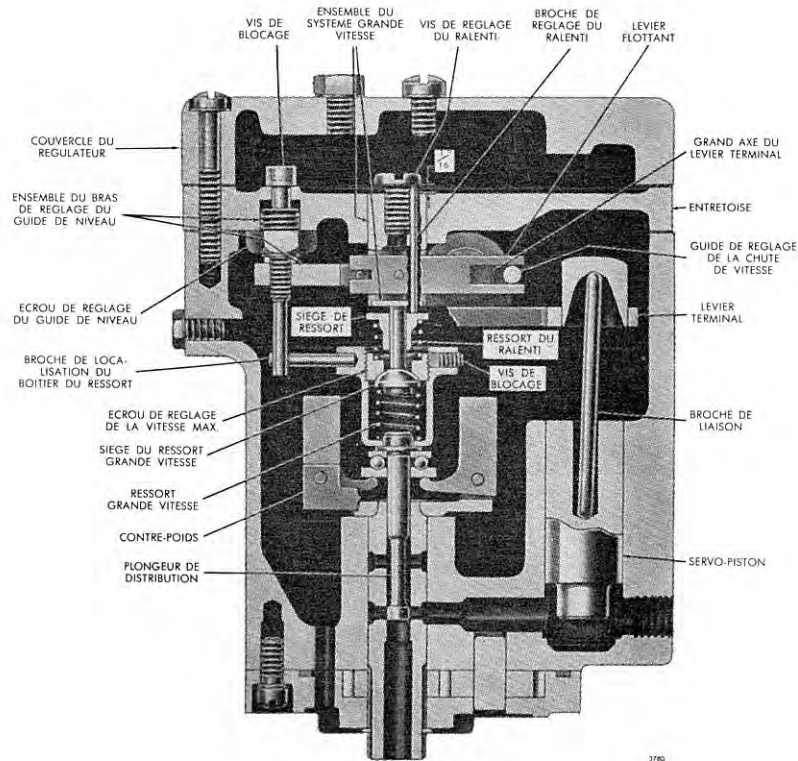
V-8 - Coupe du régulateur hydraulique à vitesse limites du 16V-71
